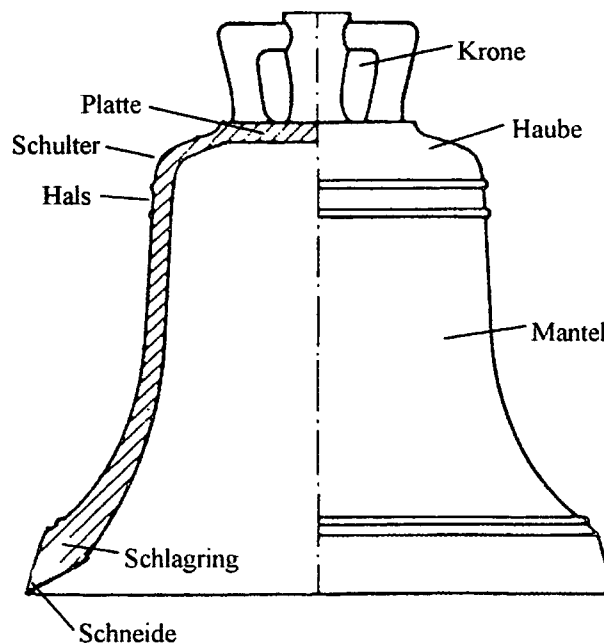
Aufbau einer Glocke (Glockenrippe)
